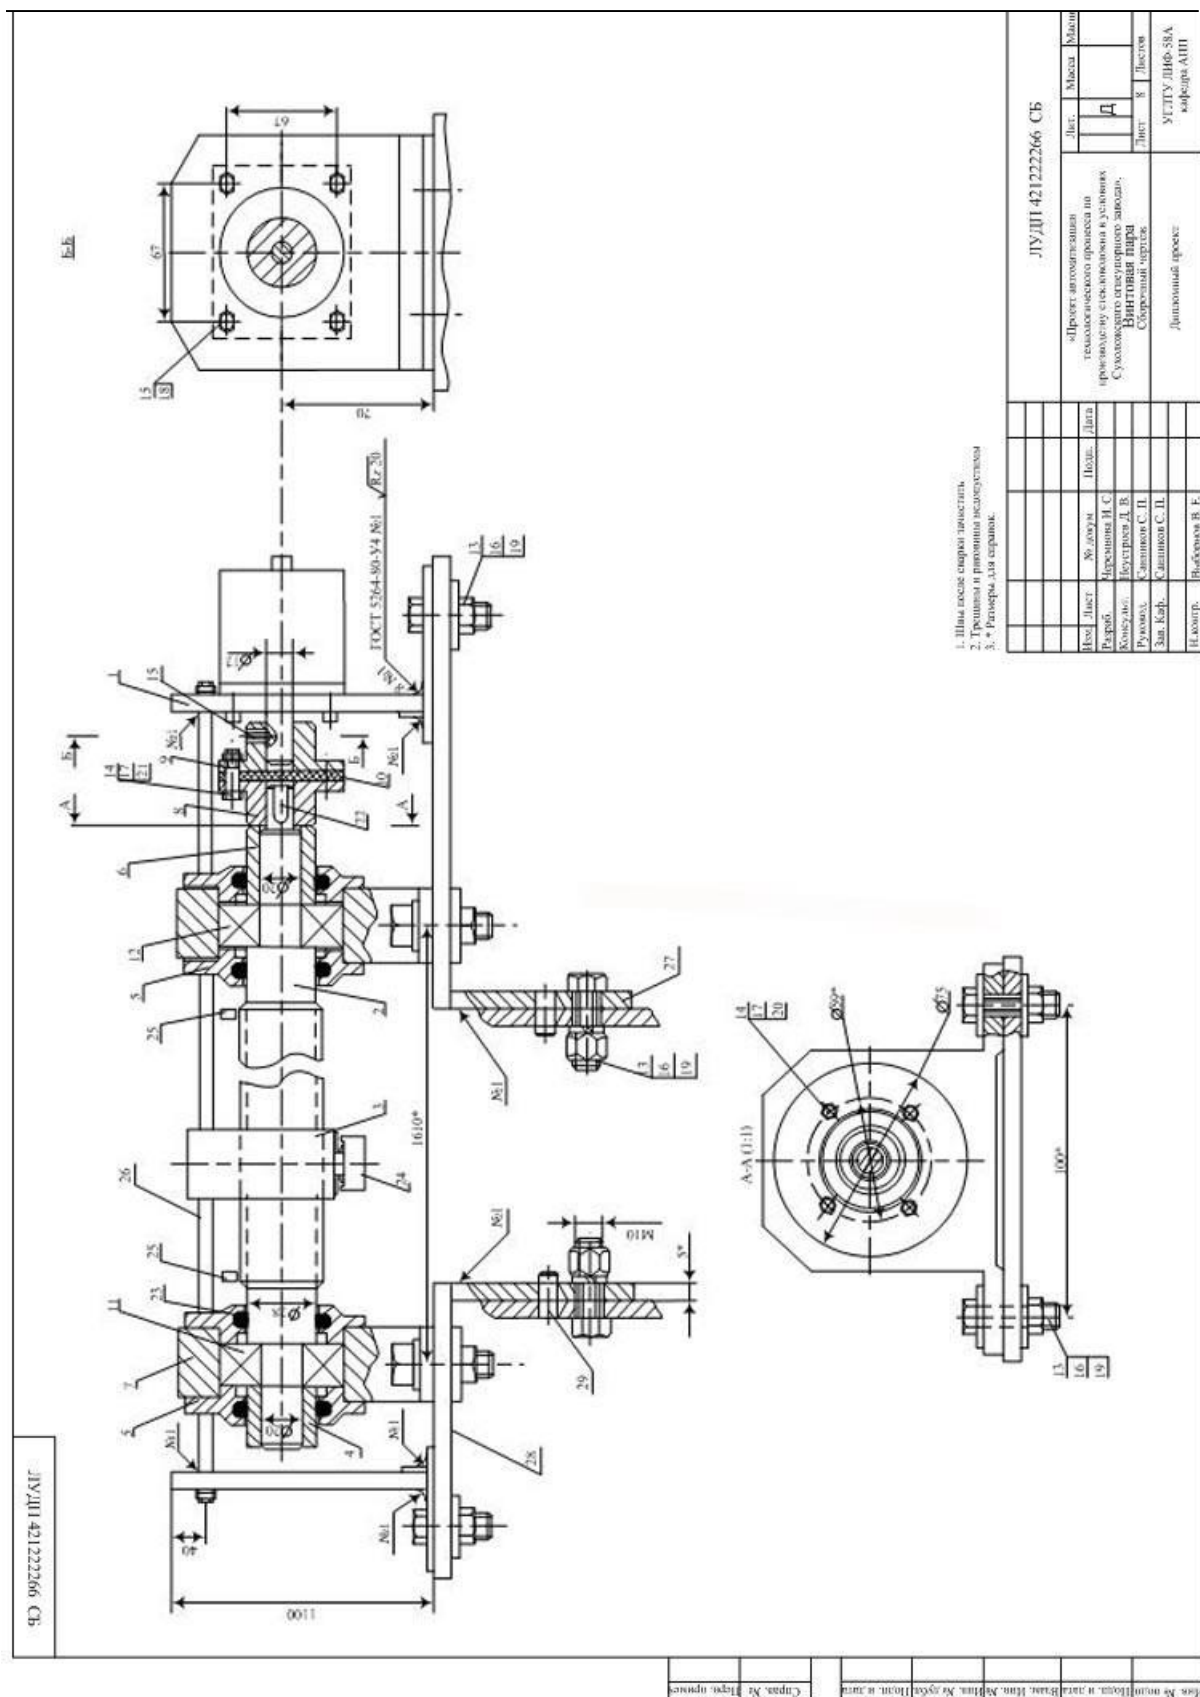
Пример сборочного чертежа расположения устройства привода рабочего инструмента
